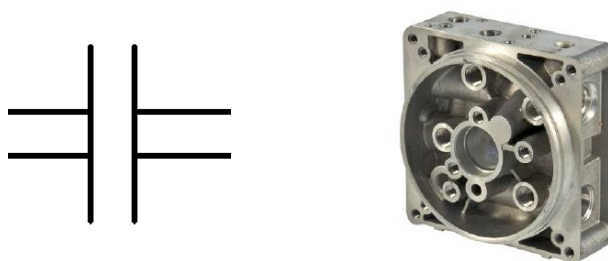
(à esquerda) Símbolo de acoplamento; (à direita) Acoplamento entre o motor elétrico *DC* e o depósito, [52].
